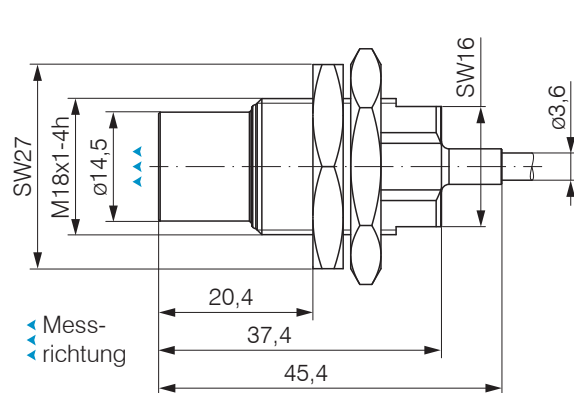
Maßzeichnung Sensoren ES-U6-C-CaX/mB0
